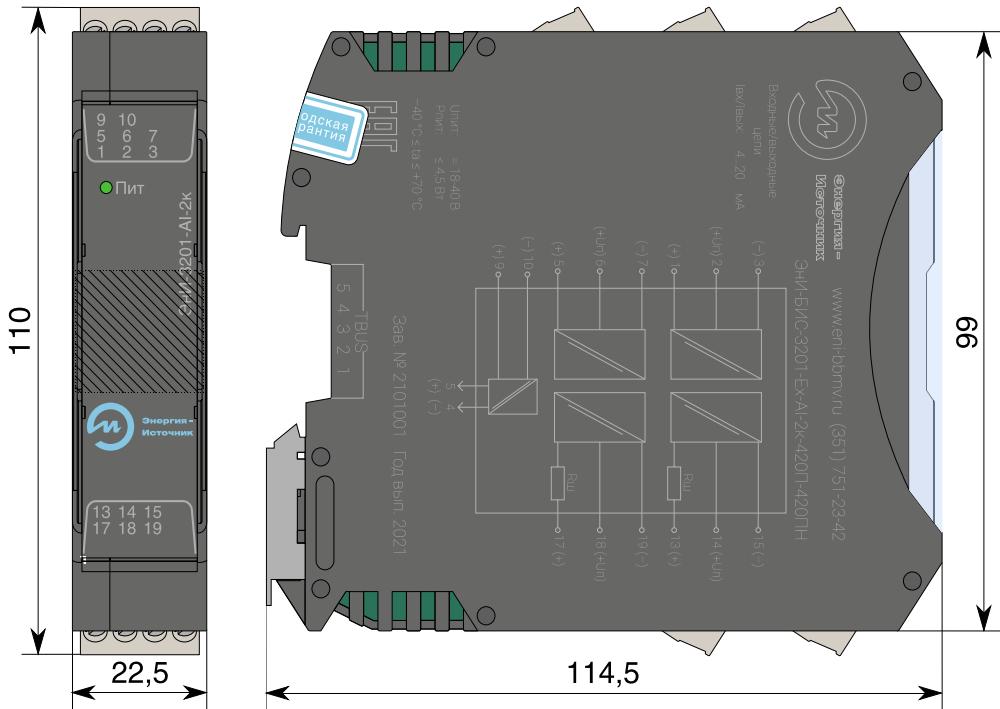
Габаритные размеры модулей с разъемами с винтовыми клеммниками
